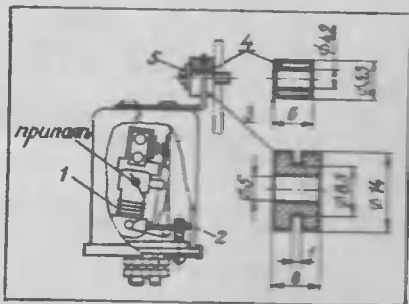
Реле РС-57В в детали его крепления: 1 — добавочное сопротивление; 2 — регулировочный винт; 3 — резиновая втулка; 4 — распорная втулка; 5 — болт М4.
